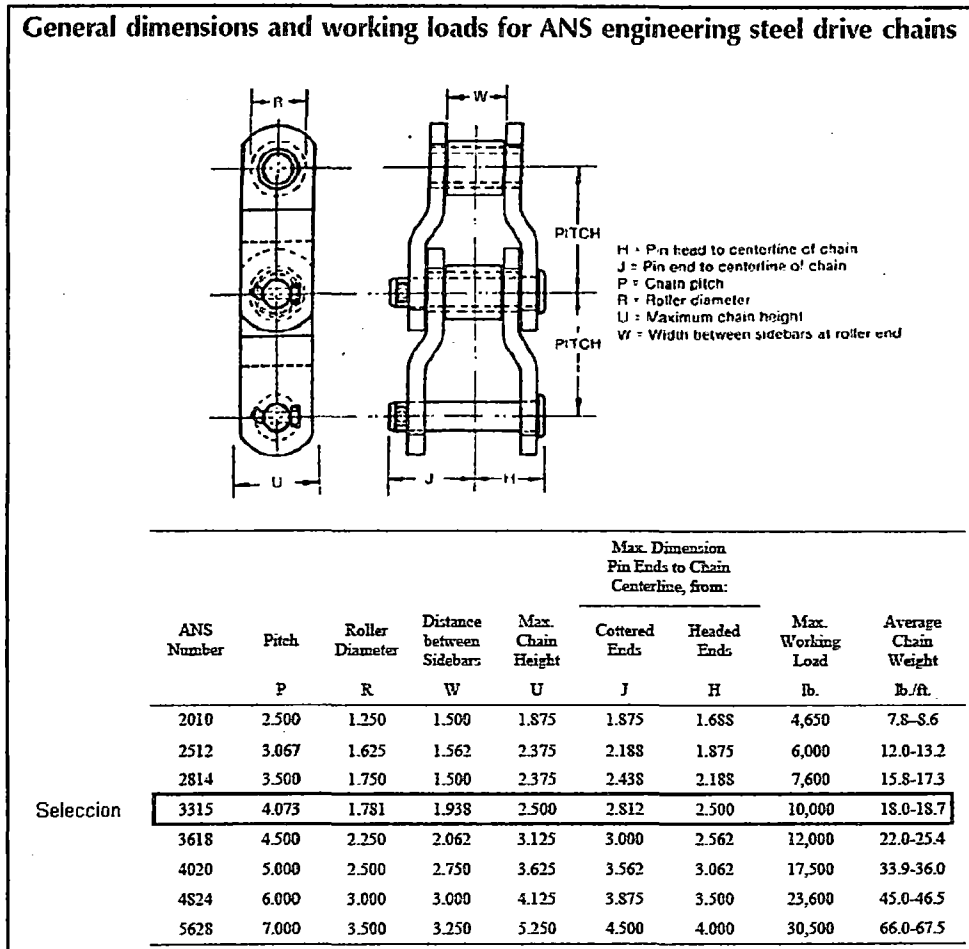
Dimensiones Cadena Tipo Engineering Steel Drive Chains
